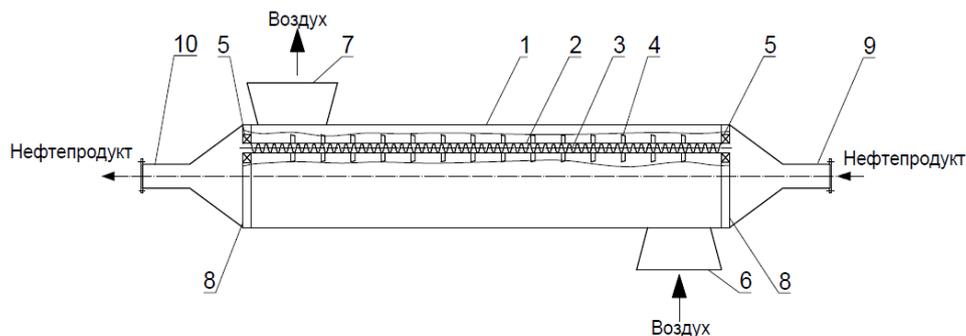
Схема нового аппарата воздушного охлаждения: 1 – корпус аппарата; 2 – вращающиеся внутренние трубы; 3 – шнек; 4 – вентилятор; 5 – подшипник; 6 – диффузор; 7 – конфузор; 8 – трубная решетка; 9 – патрубок входа нефтепродукта; 10 – патрубок выхода нефтепродукта.
